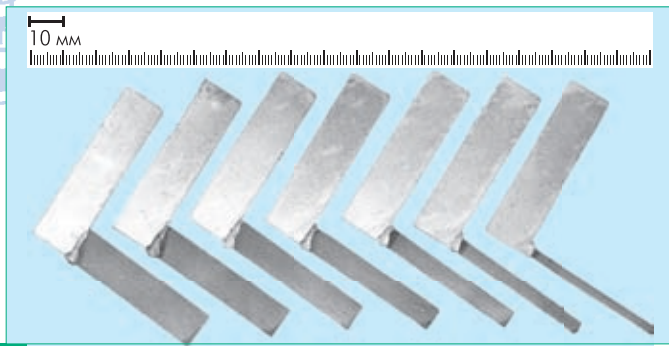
Макрошлиф углового разностенного соединения из высокопрочной судкорпусной стали 12ХН4МДА и коррозионно-стойкой нержавеющей стали 08Х18Н10Т. Сварка выполнялась на CO₂-лазере "Ижора-М" [11, 19]
